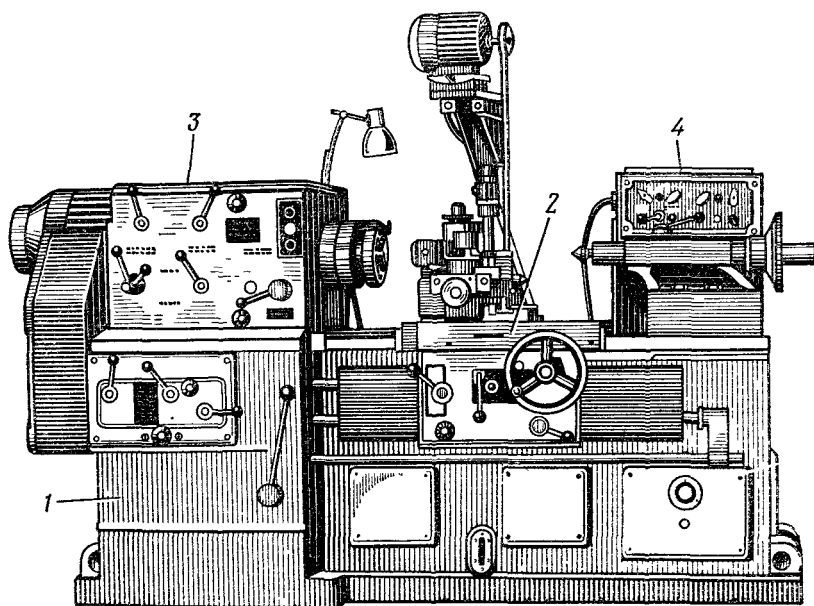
Универсальный токарно-затыловочный станок мод. 1E811
